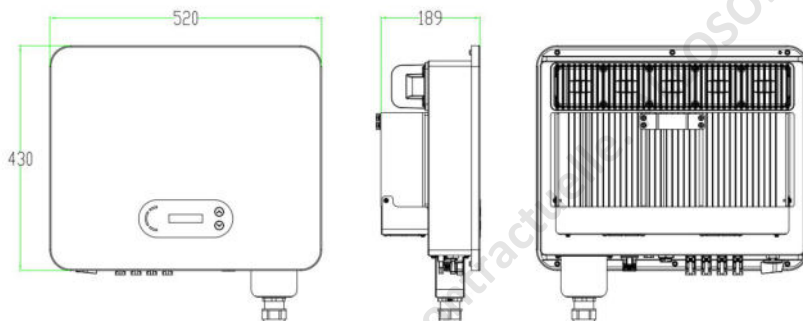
Avant, côté et arrière de la machine (15-24K)
